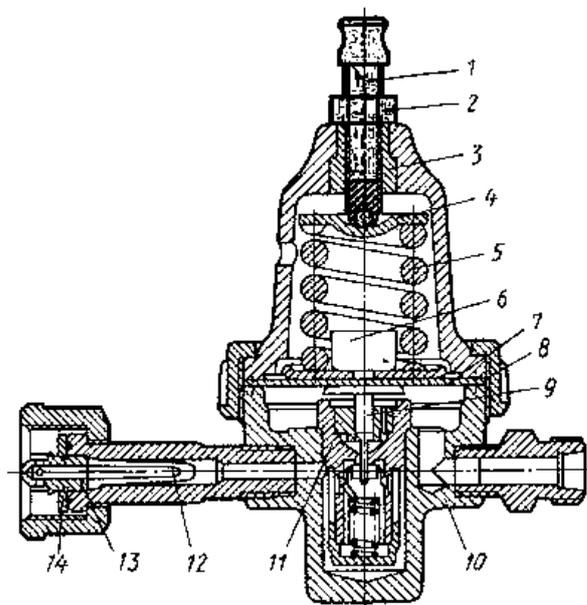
Редуктор высокого давления: 1- регулировочный винт, 2- контргайка, 3-втулка, 4-тарелка пружины, 5-пружина, 6-ограничительный клапан, 7- мембрана, 8- гайка, 9-редукционный клапан, 10-корпус редуктора, 11- корпус клапана, 12-фильтр, 13-винт, 14-шайба
